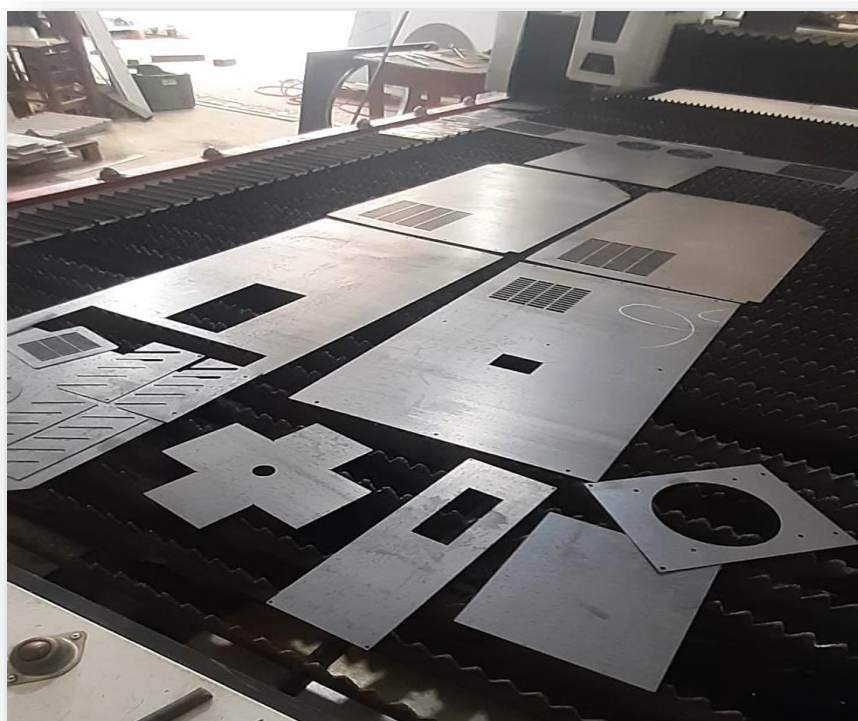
La fin de la découpe des pièces sur la tôle de 1 mm
